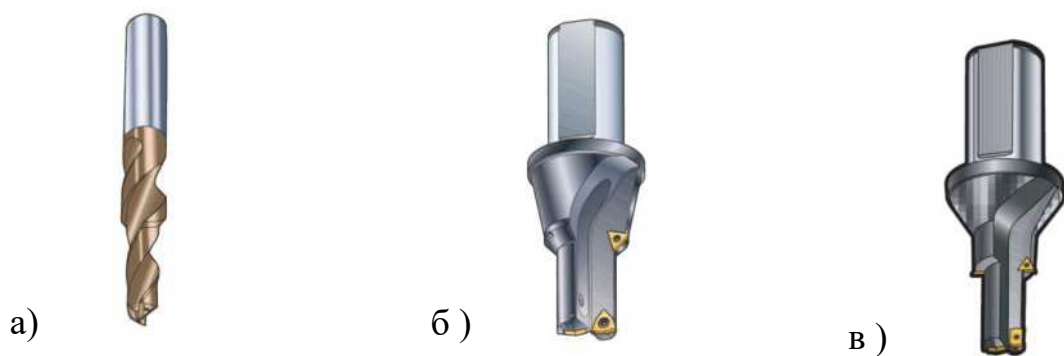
Конструктивні виконання свердел ступінчатих: а – цільне свердло для обробки отвору і зняття фасок; б, в – збірні свердла для обробки фасок і заглиблень під головку гвинта
